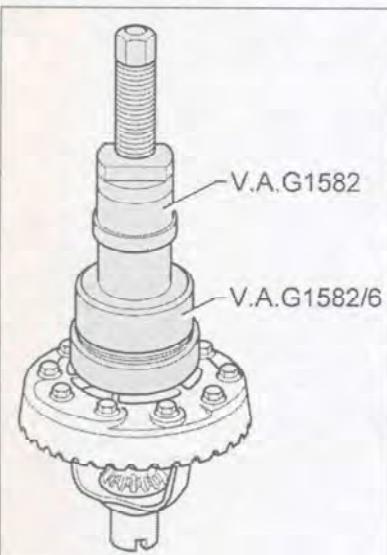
Установка внутренней обоймы малого роликоподшипника.
